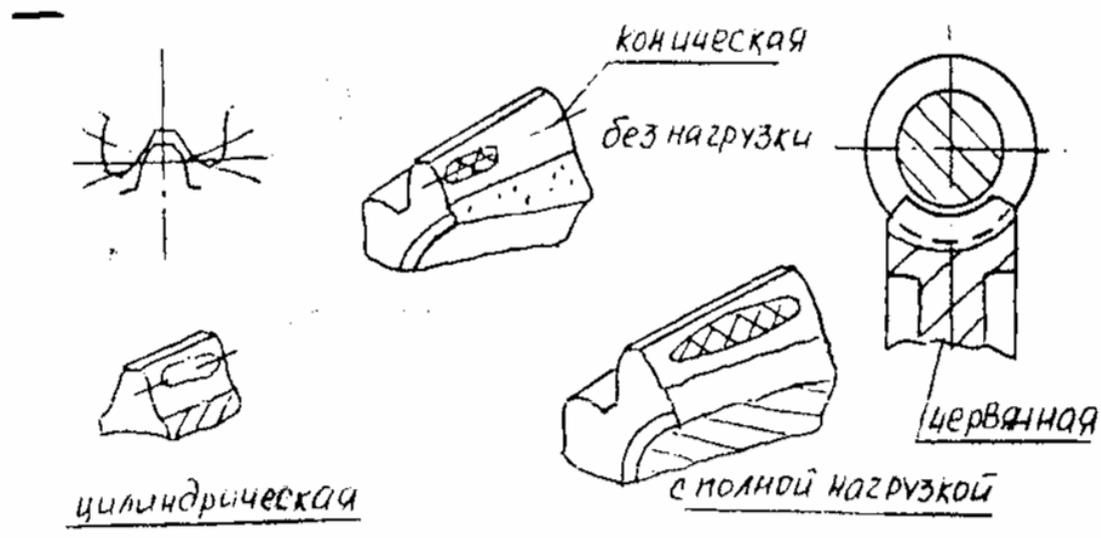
Форма площади контакта в зацеплении зубчатых колес
